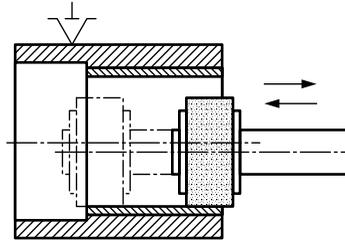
Схема обработки отверстия на внутришлифовальном станке
